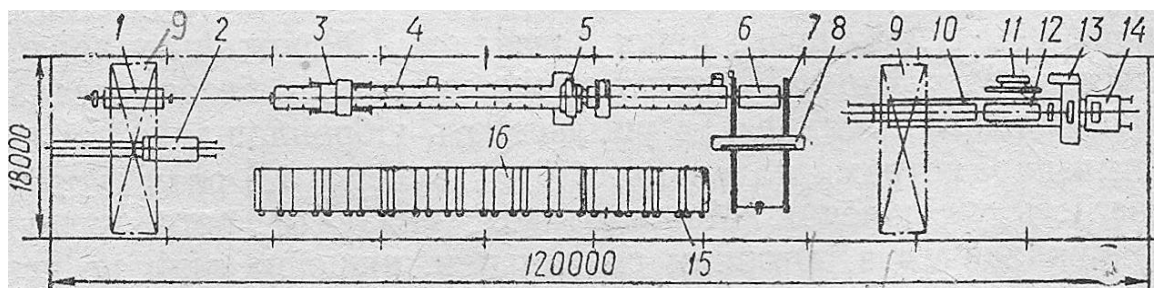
Лінія виготовлення багатопорожнинних плит з операційним рольгангом: 1- кантувач; 2 — самохідний візок; 3 — устаткування для обрізання попередньо-напружених стержнів; 4 — конвеєр підготовки піддонів; 5 — машина для очищення та змазування піддонів; 6 — підймальна секція рольганга; 7 — ланцюговий конвеєр; 8 — автоматизоване устаткування заготовлення і натягування арматури; 9 — мостовий кран; 10 — формувальна машина; 11 — вібропривантаження; 12 — віброплощадка; 13 — естакада з бункером.-накопичувачем; 14 — бетоноукладач; 15 — привод піднімання кришок камер; 16 — ямні камери ТВО
